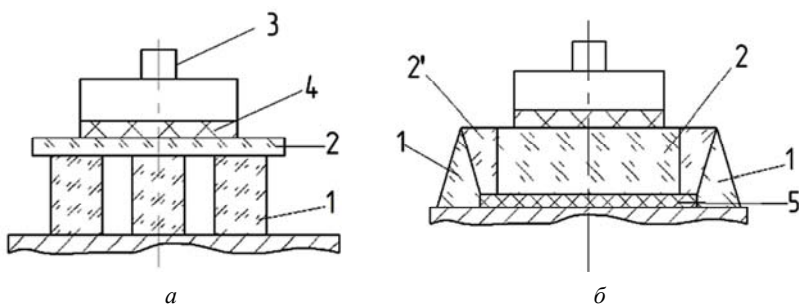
Крепление деталей методом оптического контакта с помощью контактного приспособления (*а*) и с помощью контактного приспособления и переходных «сухарики» (*б*):
